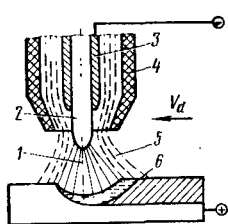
Схема сварки в атмосфере защитных газов:
